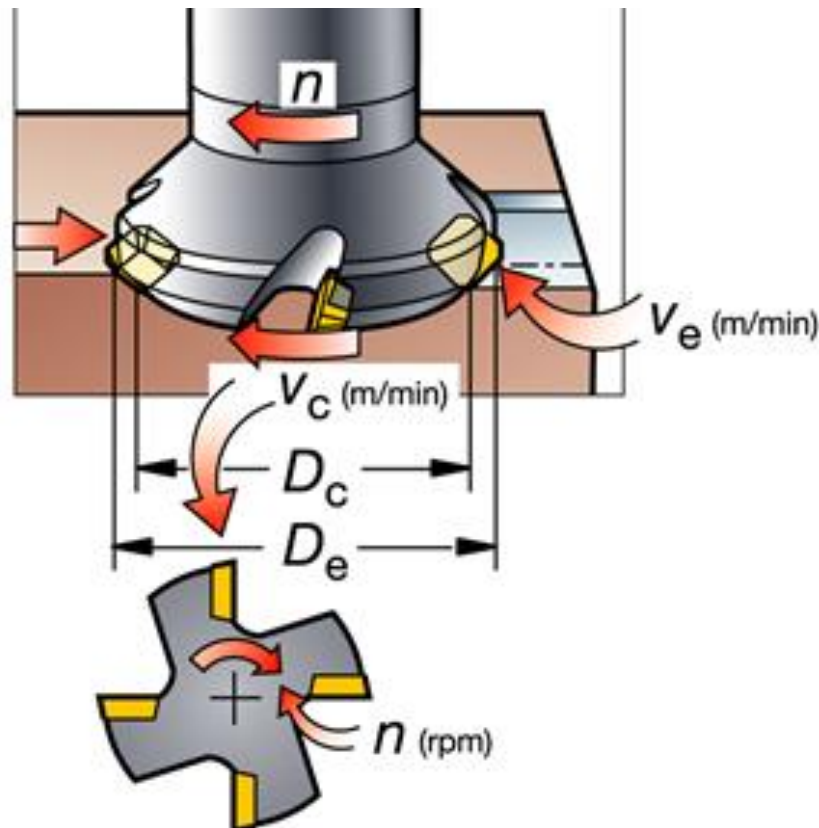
Режими і параметри торцевого фрезерування
